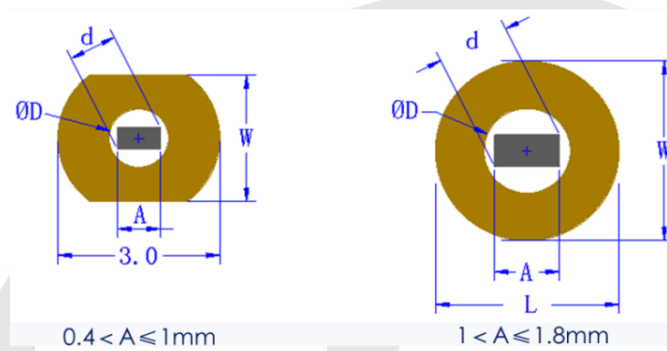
扁形引脚焊盘尺寸标注
